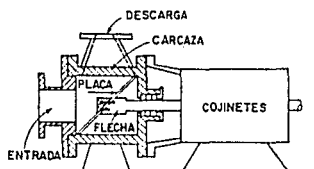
BOMBA DE ROTOR INCLINADO
